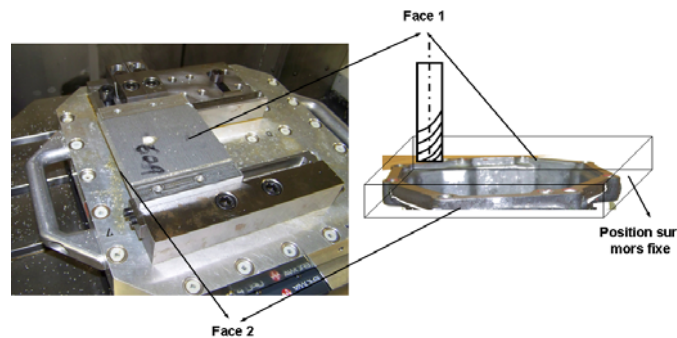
La position de la pièce brute sur le montage d'usinage et les faces 1 et 2
